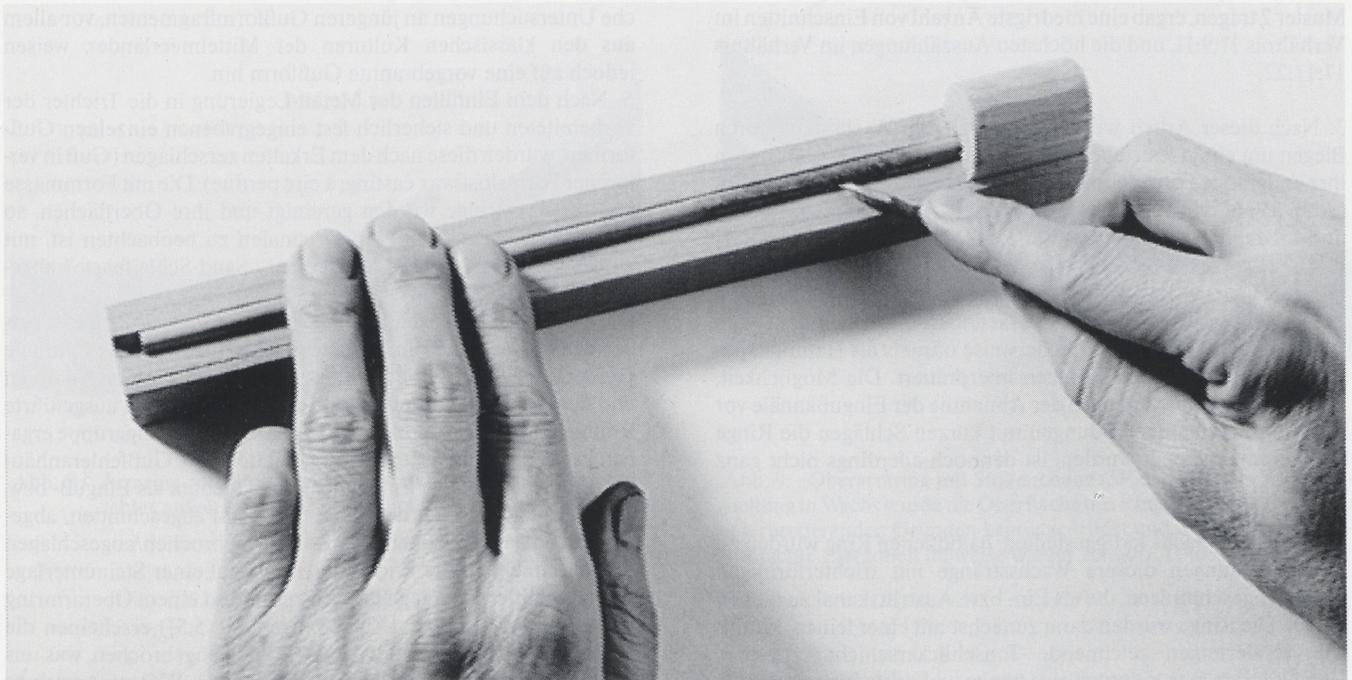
Drehbank wie auf Abb. 3, jedoch ohne Durchführung des Werkstückes vorne und ohne Führungsnuten für das Werkzeug. Das Werkstück wird nur mit den aufgelegten Fingern gedreht, das Werkzeug (Messer oder Stichel) ohne Führung leicht dagegen oder von oben aufgedrückt.
